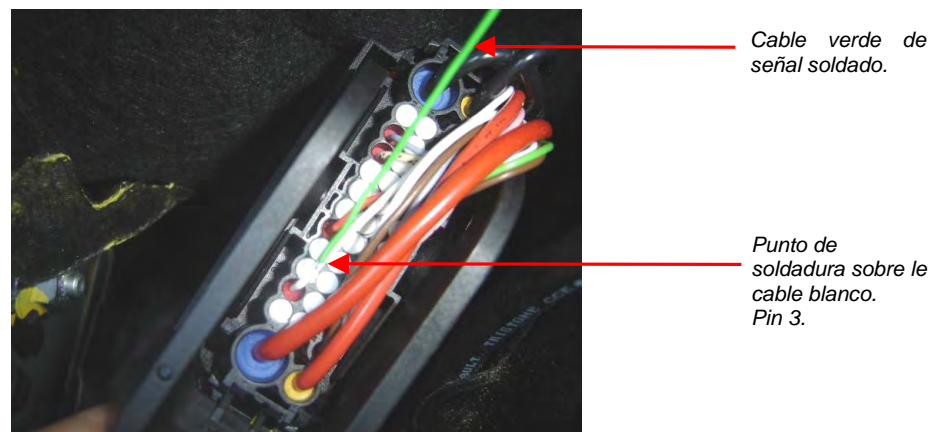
Vista del conector con el cable verde de señal soldado.
